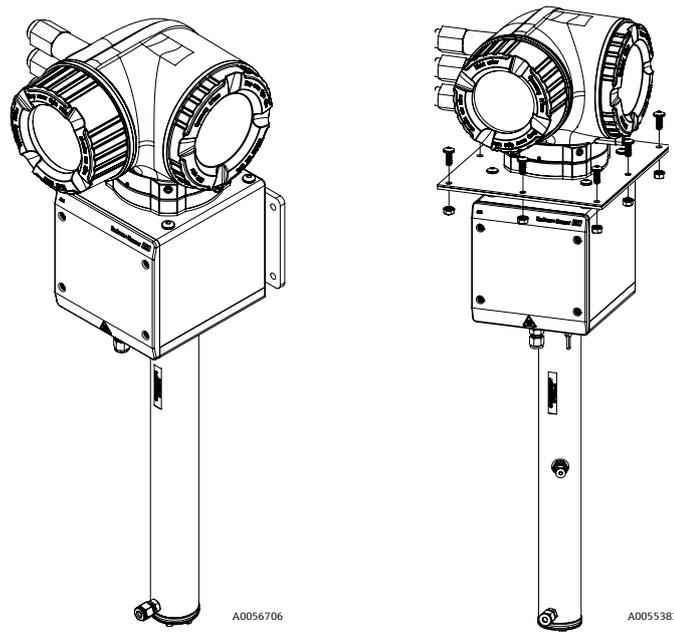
Bügel und Befestigungsmaterialien für eine Montage über die Geräterückwand und auf einem Befestigungsblech
